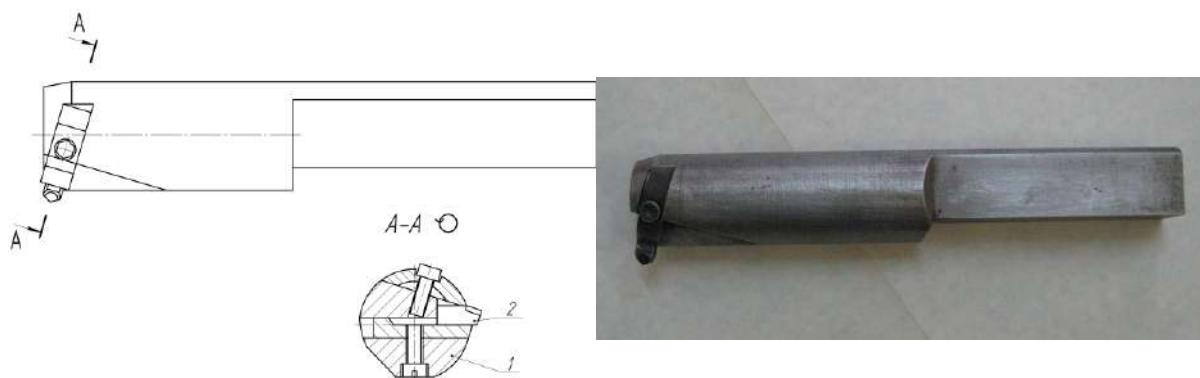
Конструкция и общий вид расточного резца с механическим креплением универсальной резцовой вставки: 1 – державка; 2 – резцовая вставка
